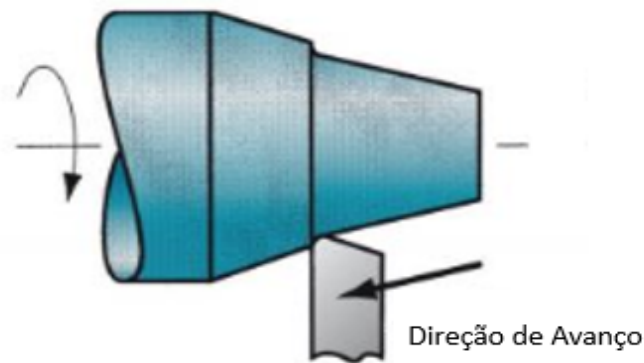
Torneamento cônico (GROOVER, 2014)
